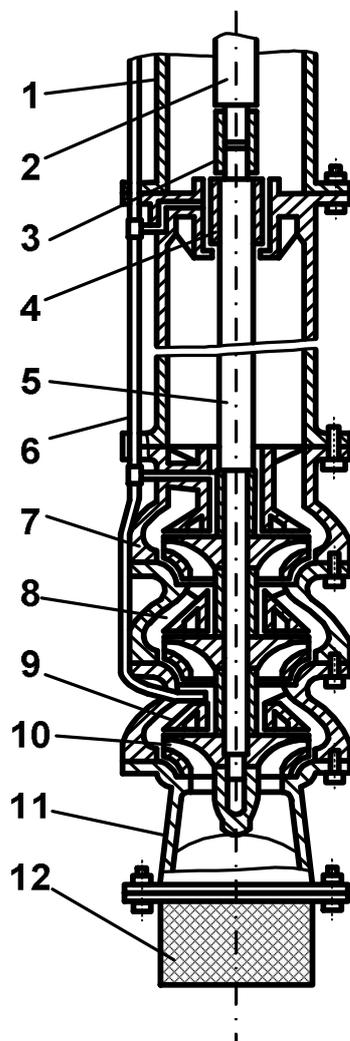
Насосный узел агрегата типа ЦТВ: 1 – напорный трубопровод; 2 – трансмиссионный вал; 3 – жесткая соединительная муфта; 4 – направляющий подшипник; 5 – вал насоса;
